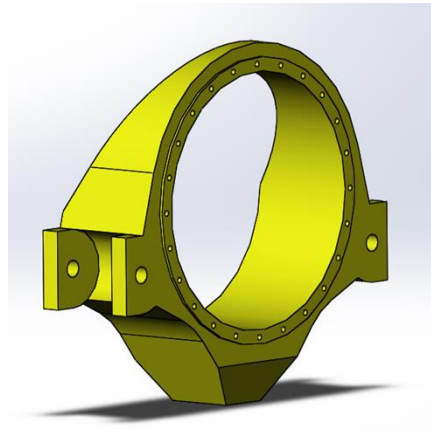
Barra o strut vertical, FUENTE: SOLIDWORKS
